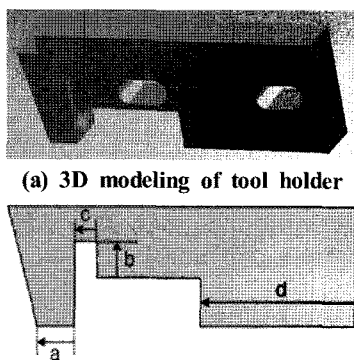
(a)은 유연 힌지구조를 이용하여 PZT tool holder를 3D로 모델링 한 것이다. 한 개의 Notch를 사용하여 형상을 모델링 하였으며, 3D 모델링은 Pro-Engineer를 사용하였다.
